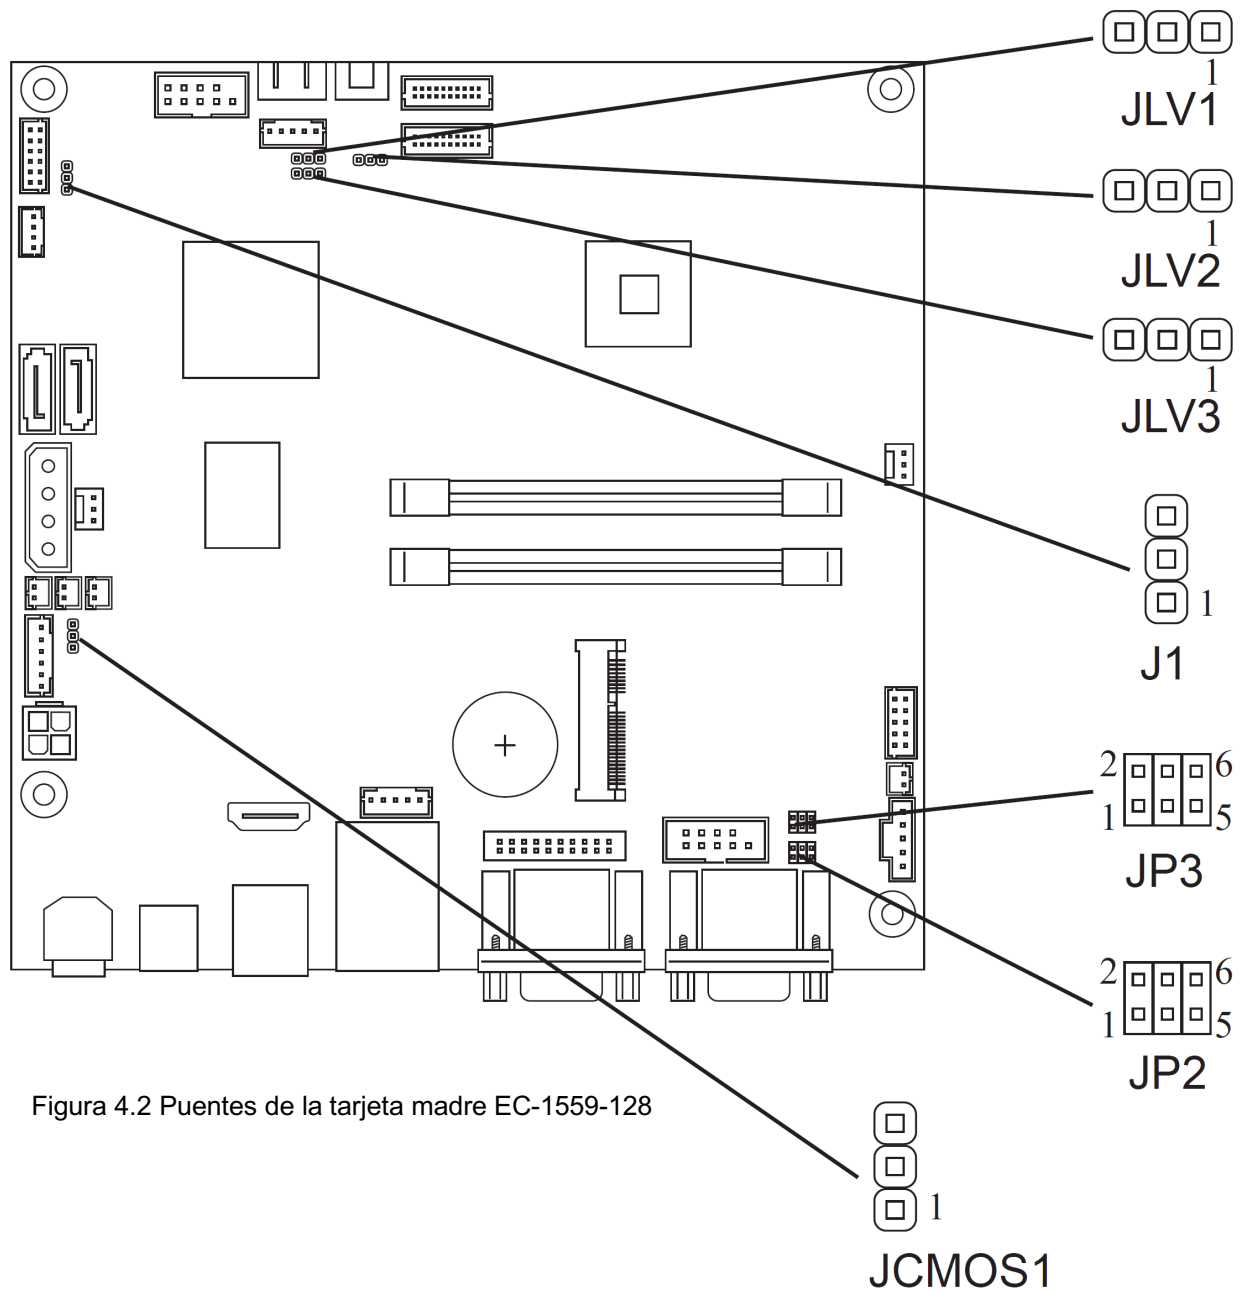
Puentes de la tarjeta madre EC-1559-128
